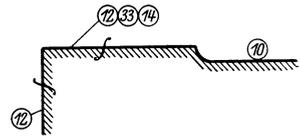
Bearbeitungsangaben des Schweizer Normenausschusses.
